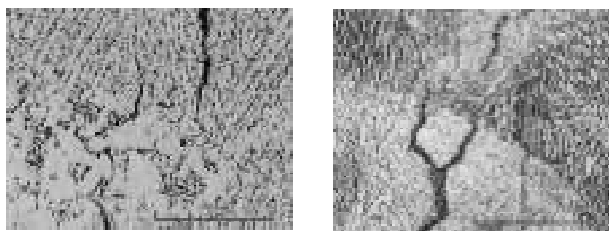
Трещины, выходящие на внешнюю поверхность по границе сварного шва и зоны термического влияния в сварных образцах-темплетах сплава ВЖЛ12Э: × 50
